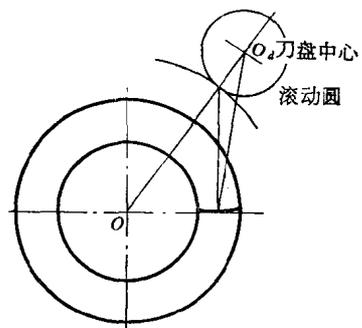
零度螺旋锥齿轮 (延伸外摆线齿)
